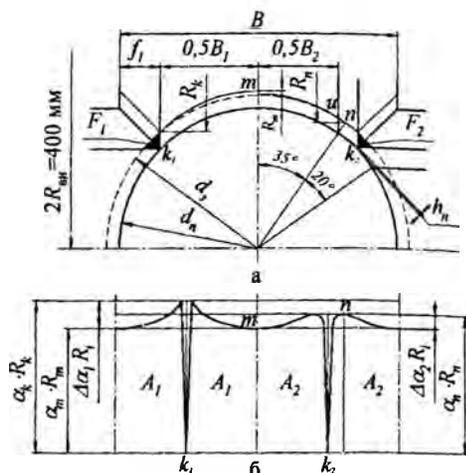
Схема калибров «круг-круг» (а) и поверхности контакта валков с заготовкой (б) в четырехвалковом калибре
